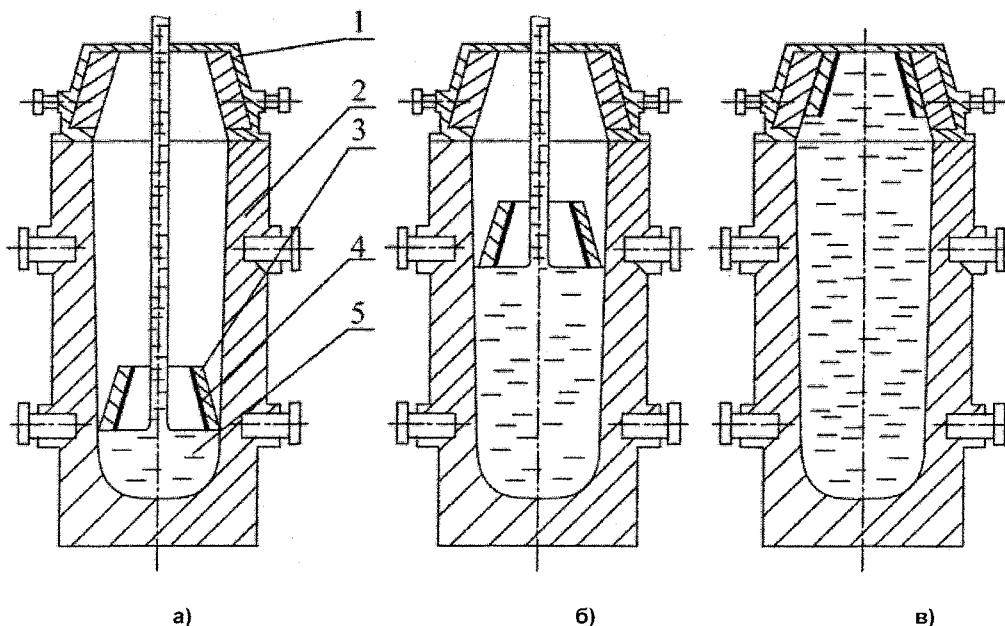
Схема разливки с использованием промежуточного элемента: а – в начальный момент разливки; б – в процессе разливки; в – в конце разливки; 1 – прибыльная надставка; 2 – изложница; 3 – экран; 4 – антипригарное покрытие; 5 – жидкий металл
